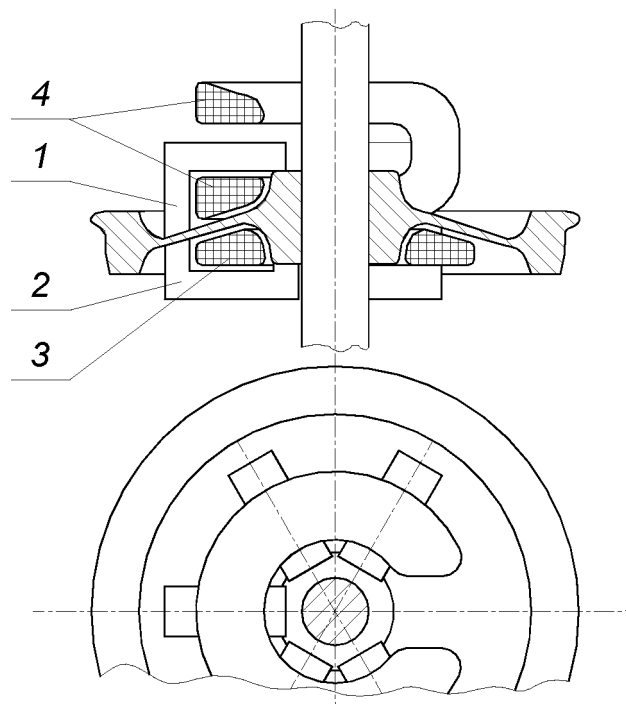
Индуктор для нагрева под разборку колесной пары тепловоза:
